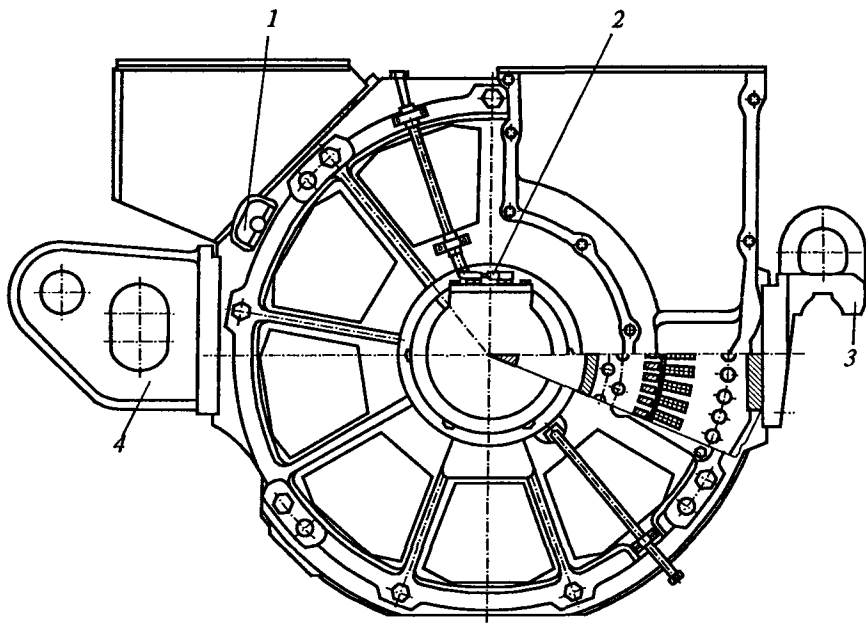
Поперечный разрез тягового электродвигателя НТА-1200:
